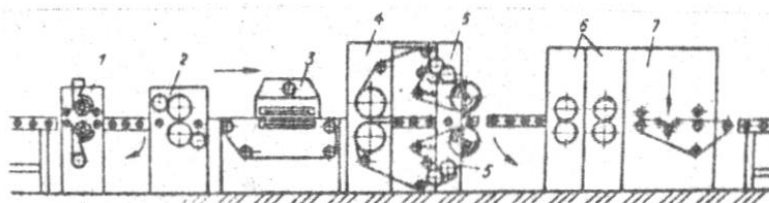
Принципова схема лінії облицювання каширування прикатуванням: 1 - щітковий верстат; 2 - нанесення клею; 3 - камера нагрівання смоли; 4 - облицювальний пристрій; 5 - нанесення затверджування; 6 - прикатувальні вали; 7 - відрізний пристрій
